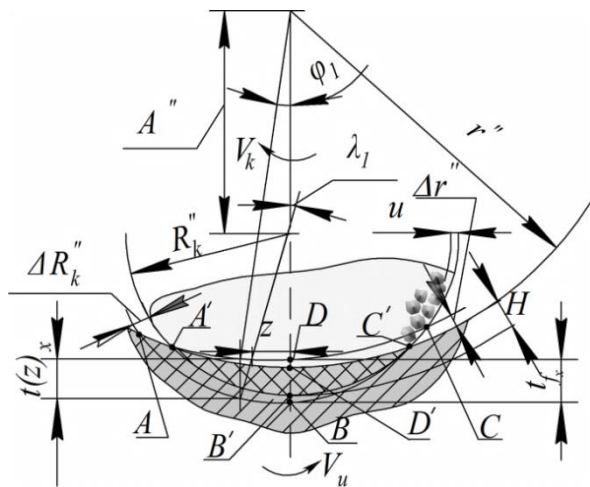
Схема - зоны контакта заготовки с конической поверхностью тарельчатого шлифовального круга при круглом внутреннем шлифовании в случае расположения оси круга под углом к оси заготовки
